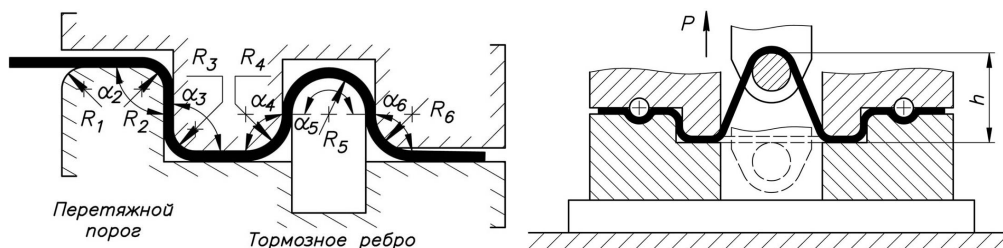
Положение фланца заготовки в начальный момент и основное время вытяжки
